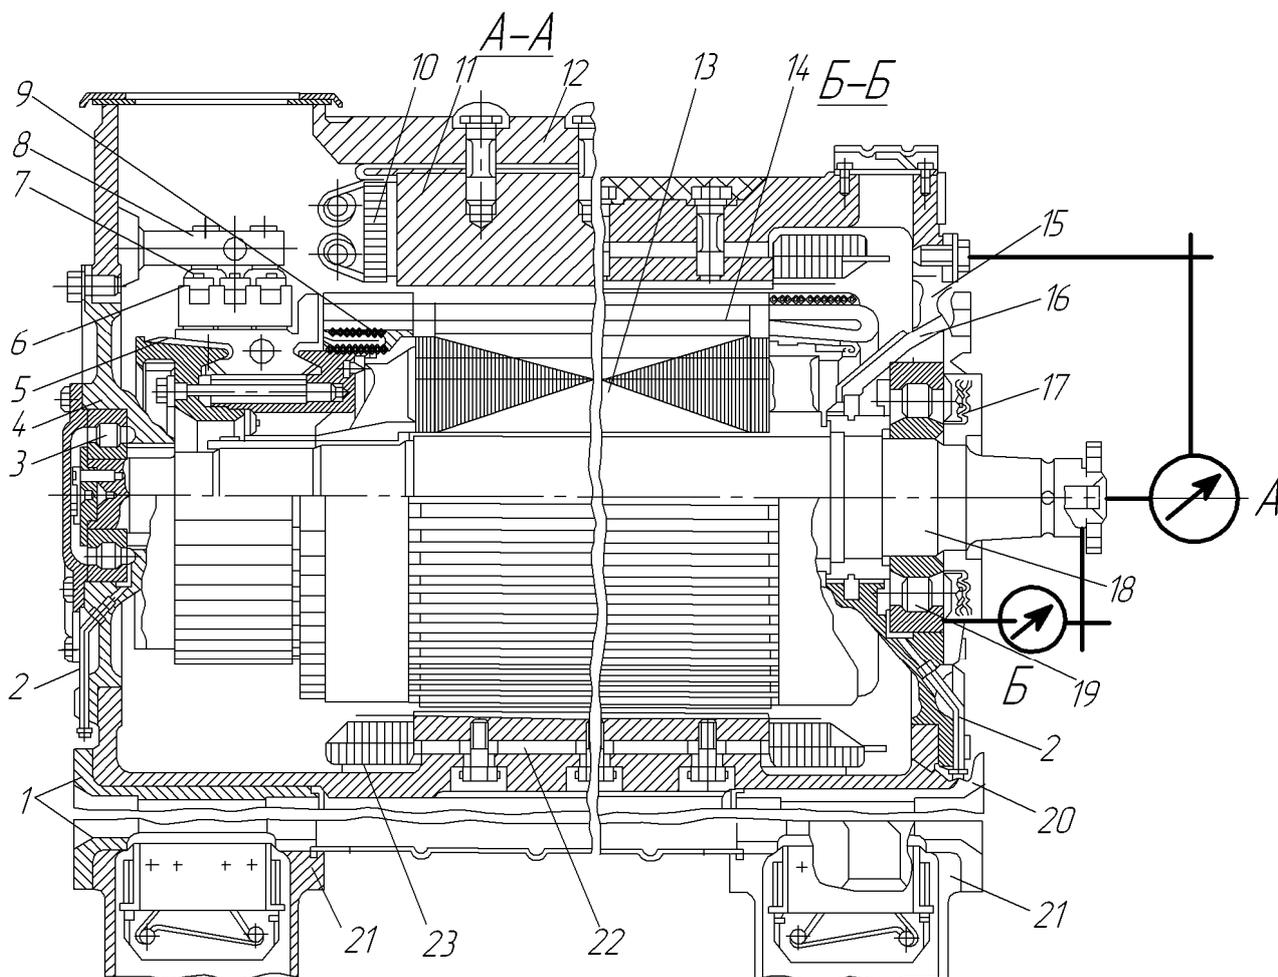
Схема оценки состояния подшипникового узла ТЭД: 1 – вкладыши моторно-осевого подшипника; 2 – трубки подачи смазки; 3, 19 – роликовые подшипники; 4, 15 – щиты подшипниковые передний и задний; 5 – коллектор; 6 – щеткодержатель; 7 – изолятор; 8 – кронштейн; 9 – уравниватель; 10 – катушка добавочного полюса; 11 – добавочный полюс; 12 – корпус; 13 – сердечник якоря; 14 – обмотка якоря; 16 – дренажное отверстие; 17 – уплотнительное лабиринтное кольцо; 18 – вал; 20 – пробка; 21 – корпус осевого подшипника; 22 – главный полюс; 23 – катушка главного полюса
